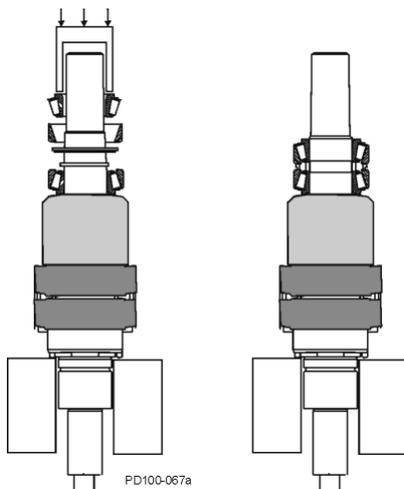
Conjunto de rodamientos de rodillos cónicos traseros
